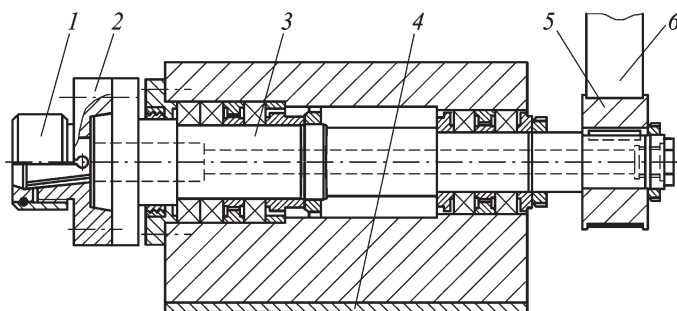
Схема комплектования нормализованными узлами базовой модели станка фирмы Tiefbohrtechnik (Германия) для сверления глубоких отверстий ружейными сверлами
